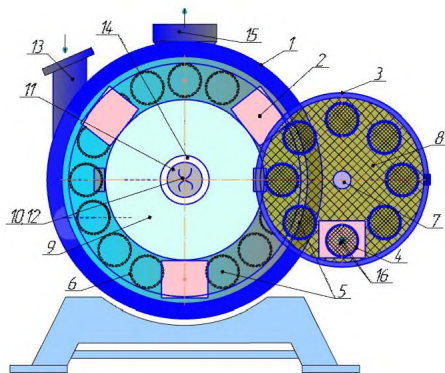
Установка для измельчения и обеззараживания зерна в электромагнитном поле сверхвысокой частоты: 1 — экранирующий корпус на станине; 2 — СВЧ генераторный блок с излучателем в диэлектрической втулке; 3 — дверь; 4 — сферическая часть резонаторной камеры; 5 — цилиндрическая часть резонаторной камеры; 6 — штифты; 7 — первый мотор-редуктор; 8 — ротор-диск малого диаметра; 9 — ротор-диск большого диаметра; 10 — шнек-дозатор; 11 — корпус шнека — запредельный волновод; 12 — второй мотор-редуктор; 13 — приемный бункер; 14 — кольцевое отверстие; 15 — патрубок для выгрузки
